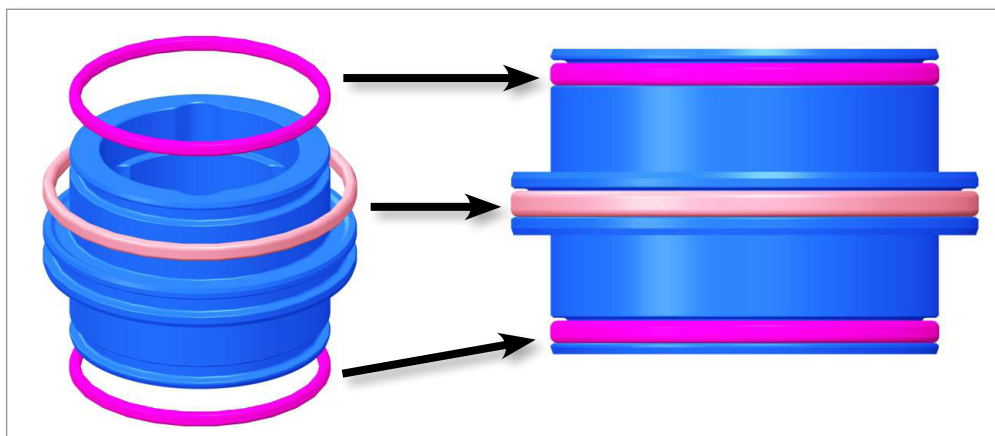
Installazione degli O-ring della parte superiore del pistone
